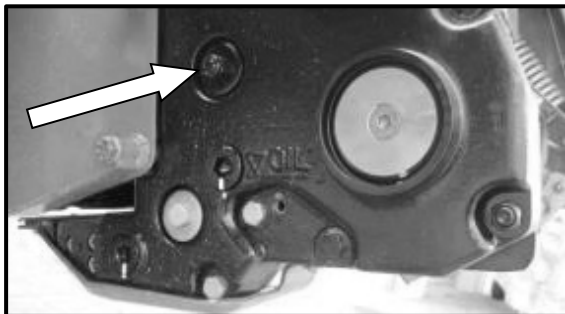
[2] Engranaje de entrada y barra de corte (2)
